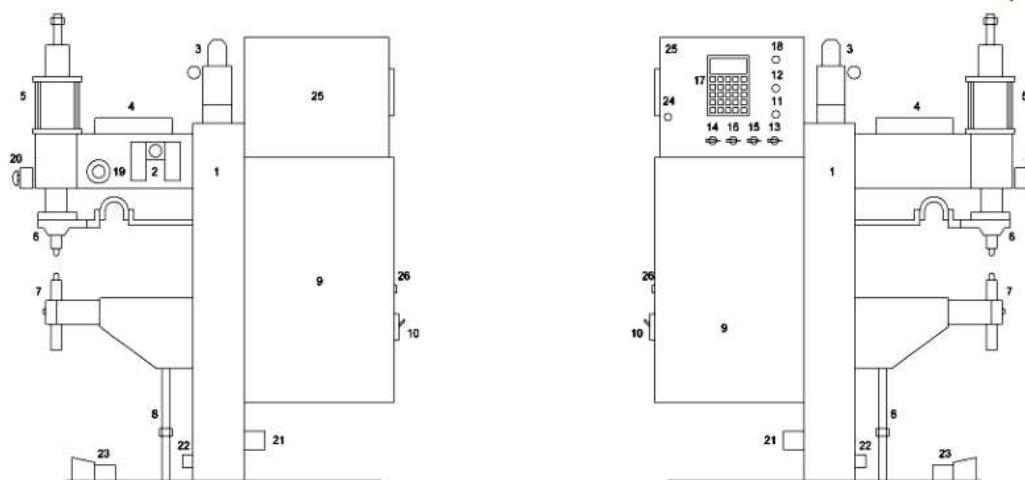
Общий вид машины контактной точечной сварки МТ-1928
